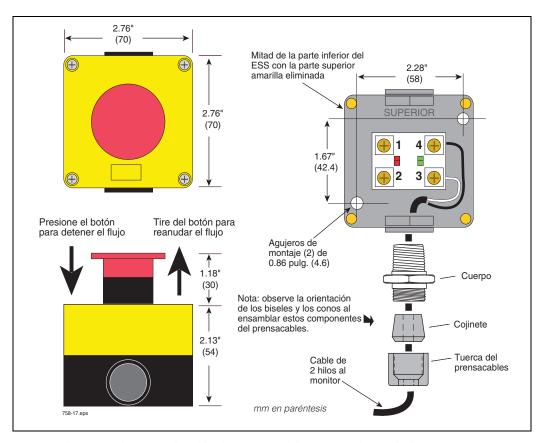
Diagrama de cableado y montaje del interruptor de parada de emergencia
